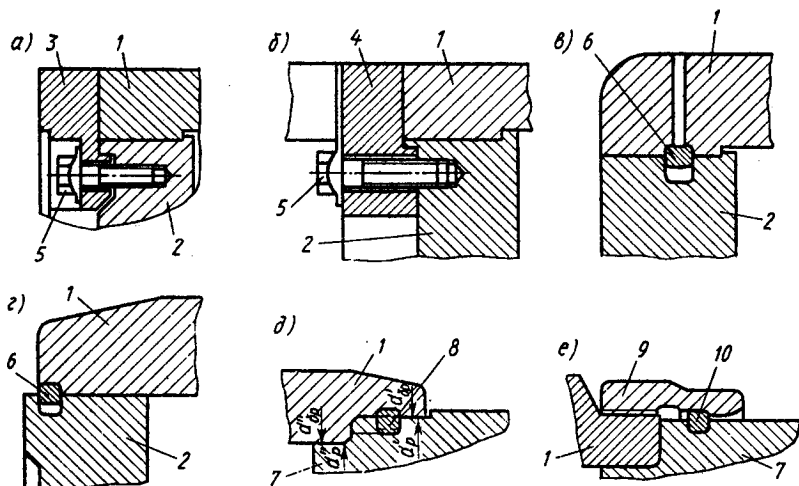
Крепление бандажного кольца от осевого сдвига:
